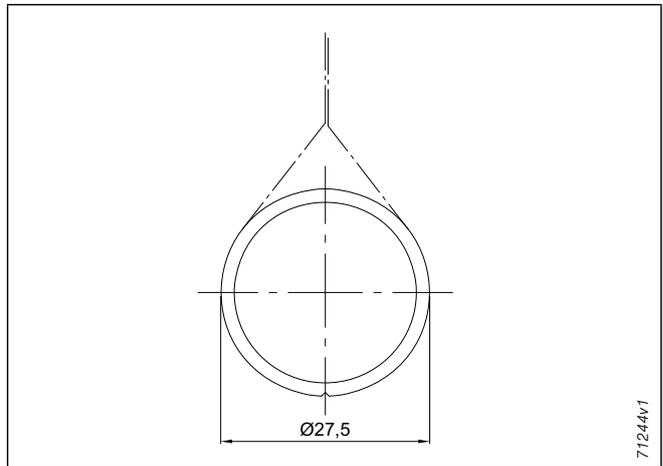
Fallprofil rund, klein, stoffumschlungen
